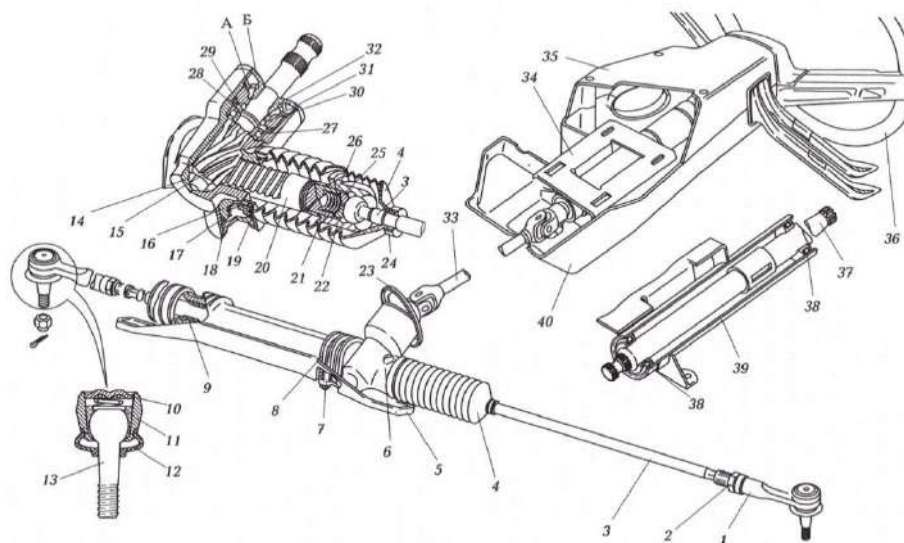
Рулевой механизм типа «зубчатое колесо — рейка»:
